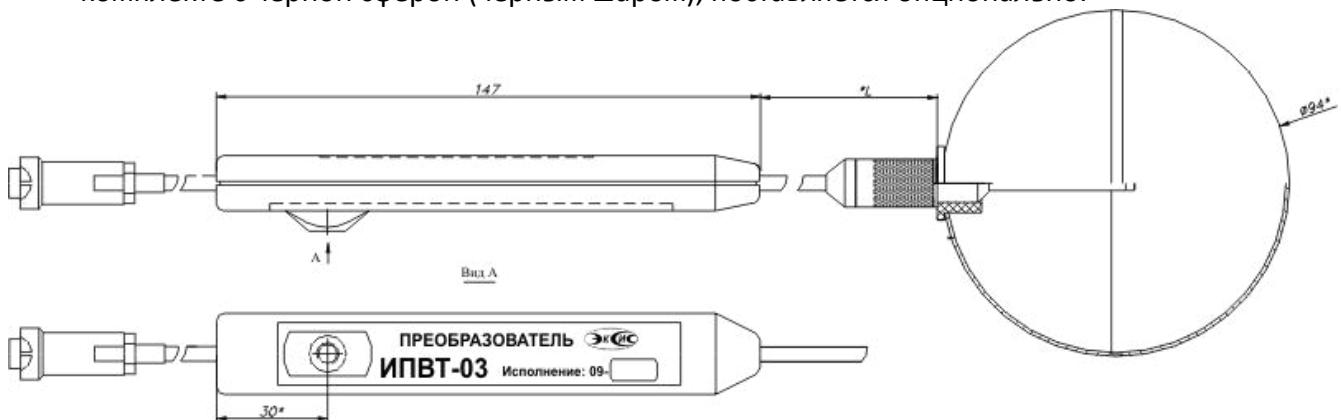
Измерительный преобразователь ИПВТ-03-09
